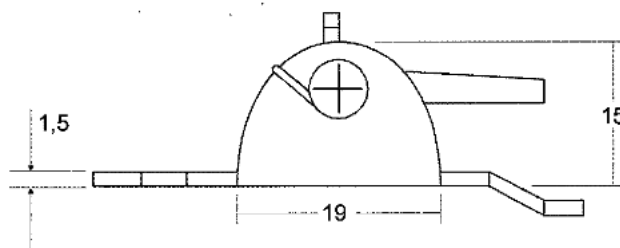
Vista lateral do ajustador metálico (medidas em mm)
